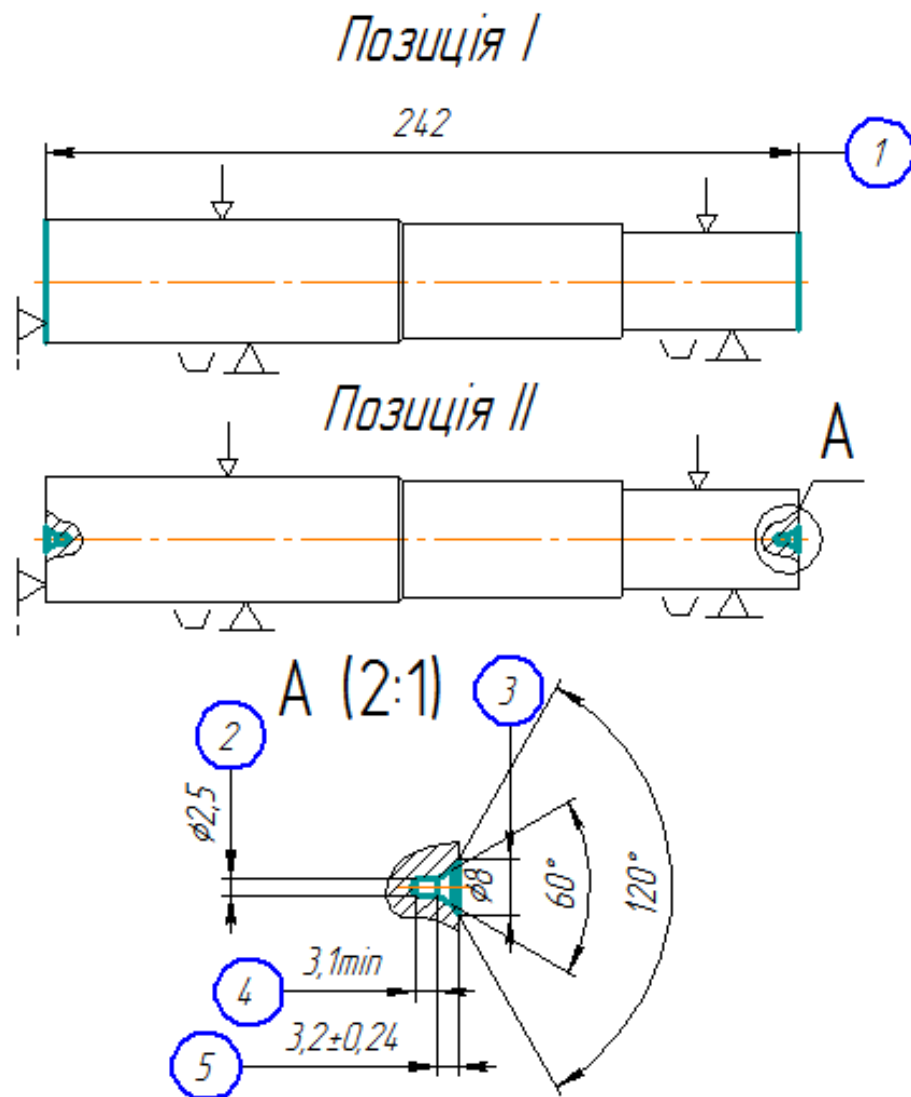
Ескіз фрезерно-центрувальної операції
